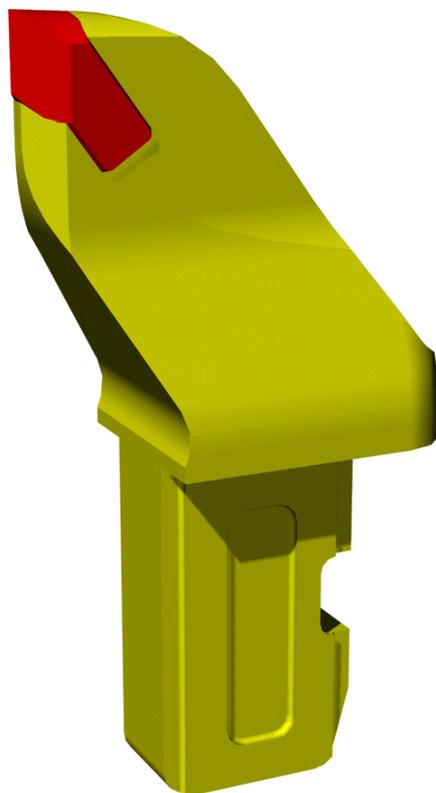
Режущий инструмент ЗРБЗ-80
